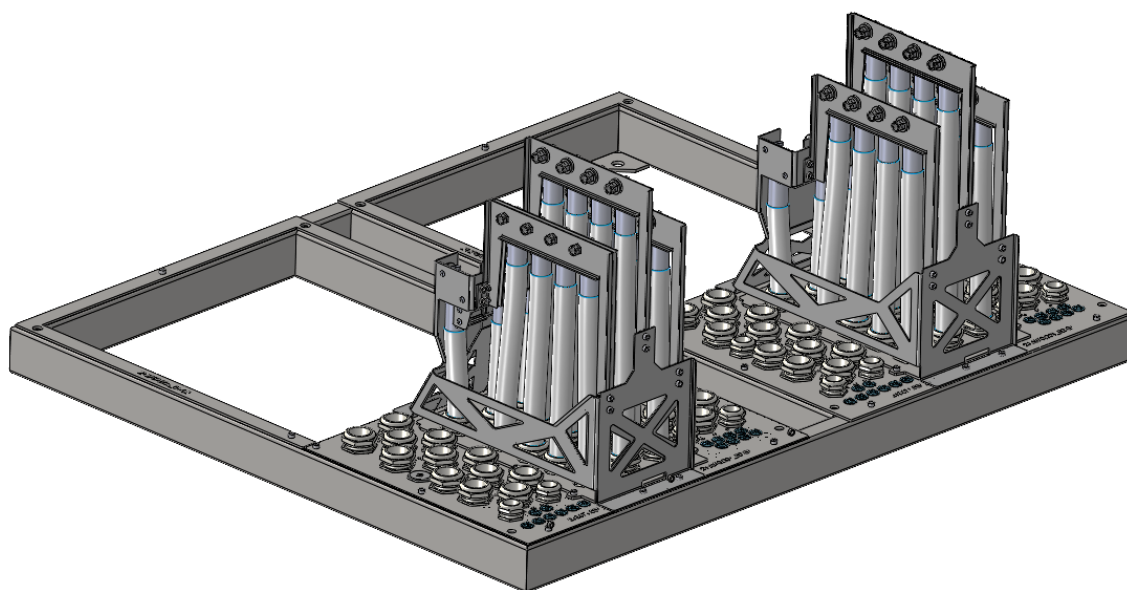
Am Cable Jig befestigte AC-Kabel
